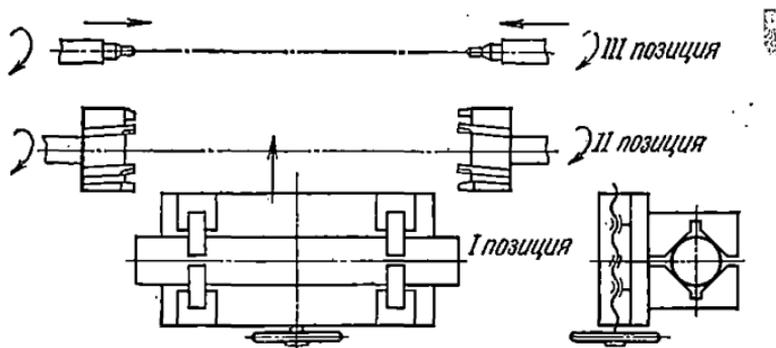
Принципиальная схема работы фрезерно-центрального станка.
